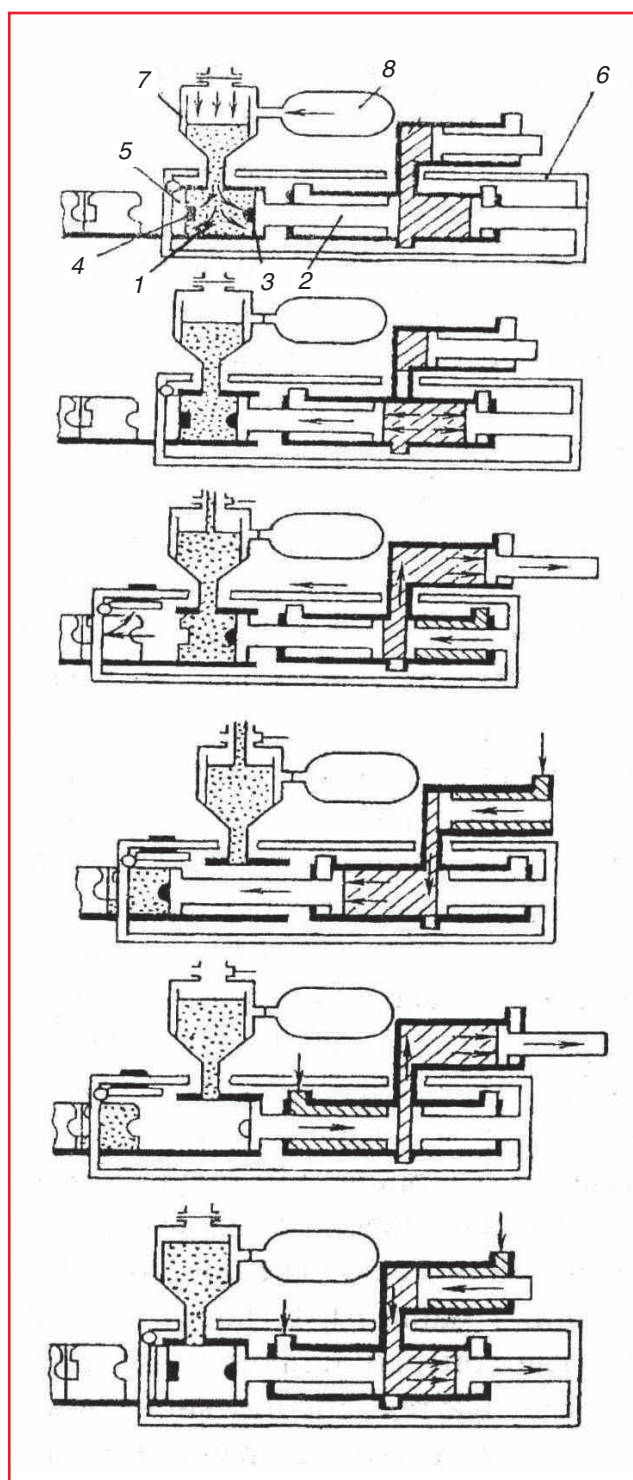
Схема работы ПП-автомата безопочных форм (а...е – последовательность операций): 1 – рабочая камера, 2 – поршень, 3 – полумодель поршневая, 4 – полумодель откидной плиты, 5 – откидная плита, 6 – корпус подвижный, 7 – пескодувный резервуар, 8 – ресивер
